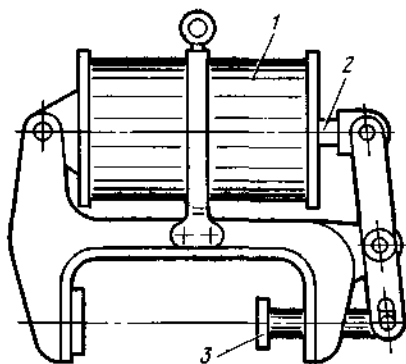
Подвесная пресс-скоба для запрессовки подшипников качения: 1 — силовой цилиндр; 2 — шток; 3 — пуансон
